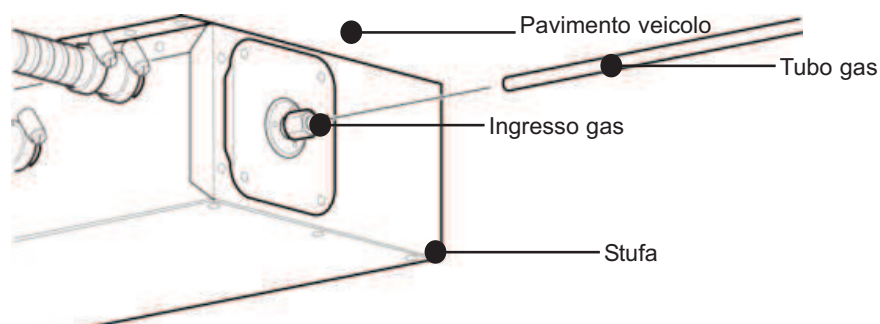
Installazione sotto il pavimento – Connessione all'alimentazione di gas
